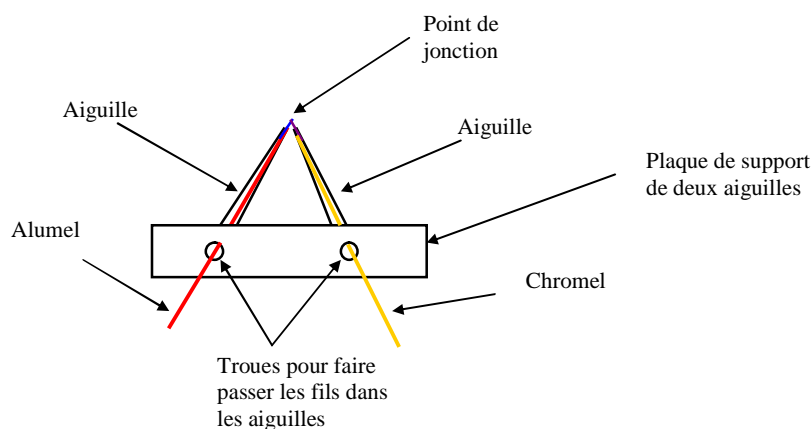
Support pour soudage des micro-thermocouples.
